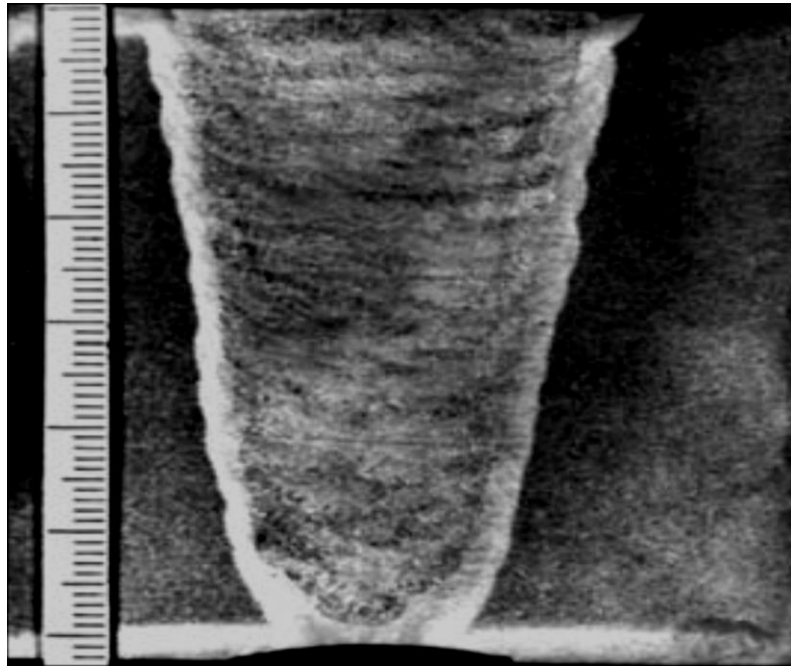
Макроструктура ($\times 2,2$) контрольного сварного соединения элементов ГЦТ Ду850, полученного ААрДС с применением сварочной проволоки Св-08Г1НМА
